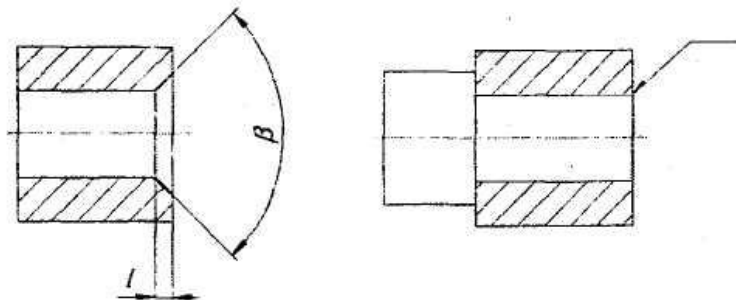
Зображення ділянки підготовки деталі до ремонту
